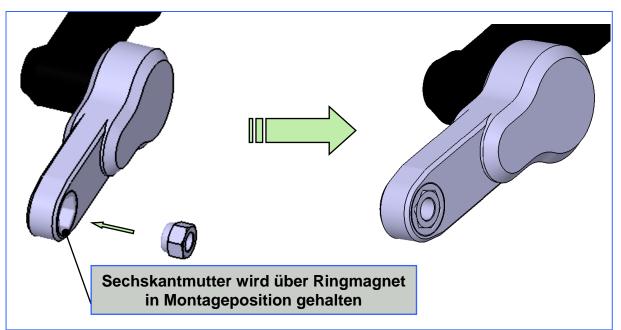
Vormontage der selbstsichernden Sechskantmutter
